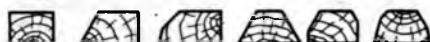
Профили заготовок, получаемых с помощью цилиндрических фрез
